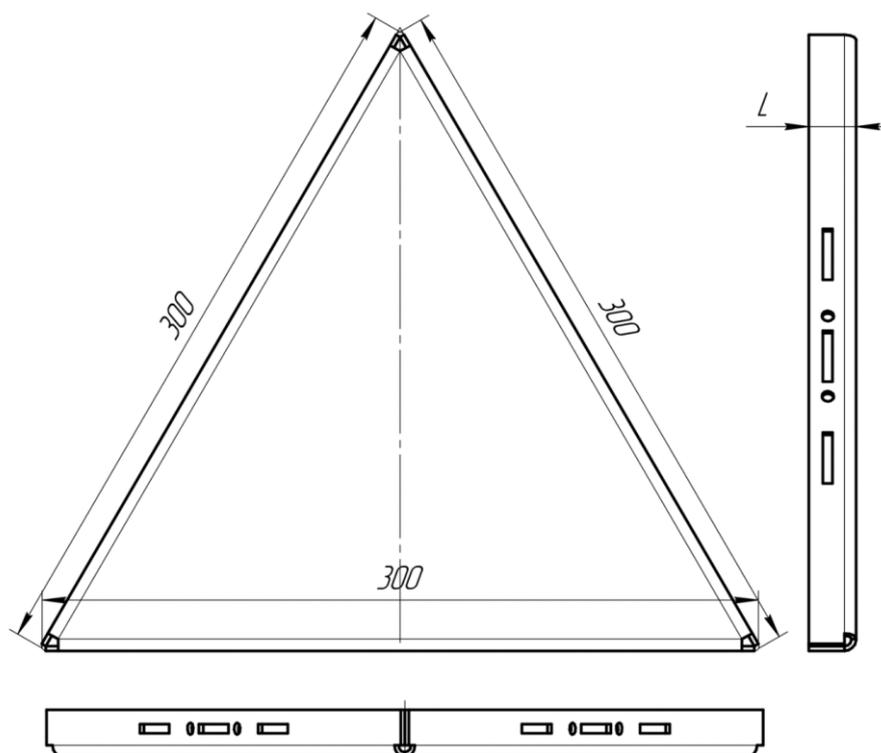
Пример конструкции знака с универсальными отверстиями для крепления.
